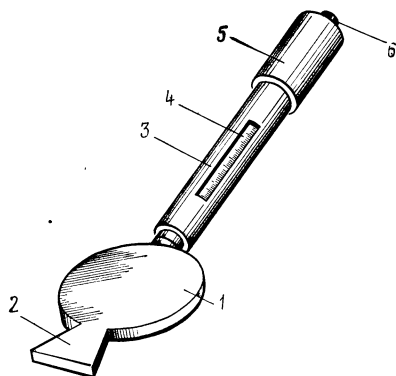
Нагреватель для сварки полиэтиленовых труб:
